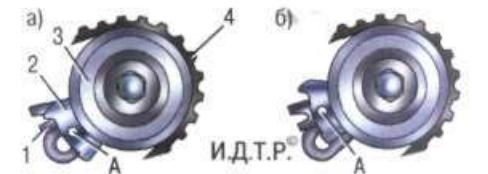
Схема контроля натяжения ремня привода газораспределительного механизма: а – положение натяжителя при регулировке натяжения ремня; б – положение натяжителя при контроле совпадения установочных меток на шкивах коленчатого и распределительного валов; 1 – кронштейн натяжного ролика; 2 – подвижная планка натяжителя; 3 – ролик натяжителя; 4 – ремень привода газораспределительного механизма; А – установочное отверстие натяжителя
